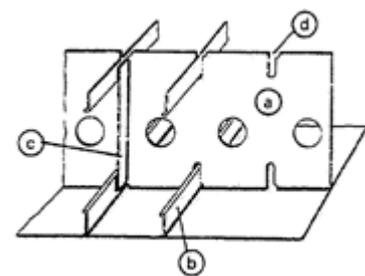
Détaille de la liaison des éléments longitudinaux avec les éléments transversaux.
